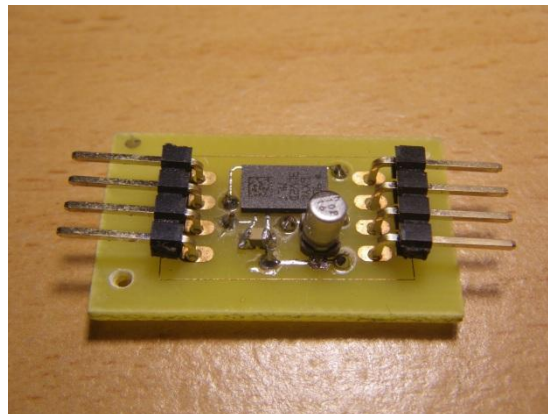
Acelerómetro LIS3LV02DL montado na PCB desenhada
